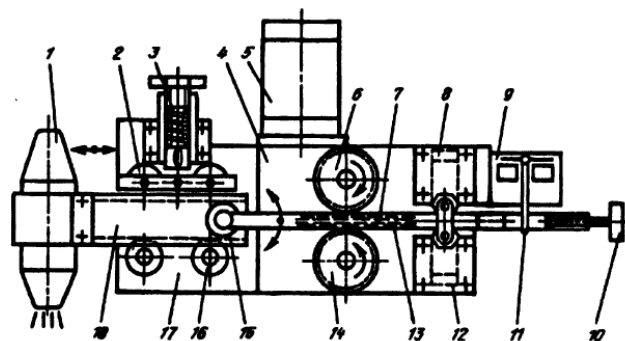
Пристрій для повідомлення коливань плазмового пальника: 1 - плазмотрон; 3,16 - роликові напрямні; 3 - пружина; 4 - редуктор; 5 - електродвигун постійного струму; 6,14 - зубчасті колеса; 7,13 - рейки; 8,12 - ефектромагніти; 9 - сигнальний блок; 10 - регулювальний гвинт; 11 - важіль; 15 - тяга; 17 - кронштейн; 18 - повзун.
